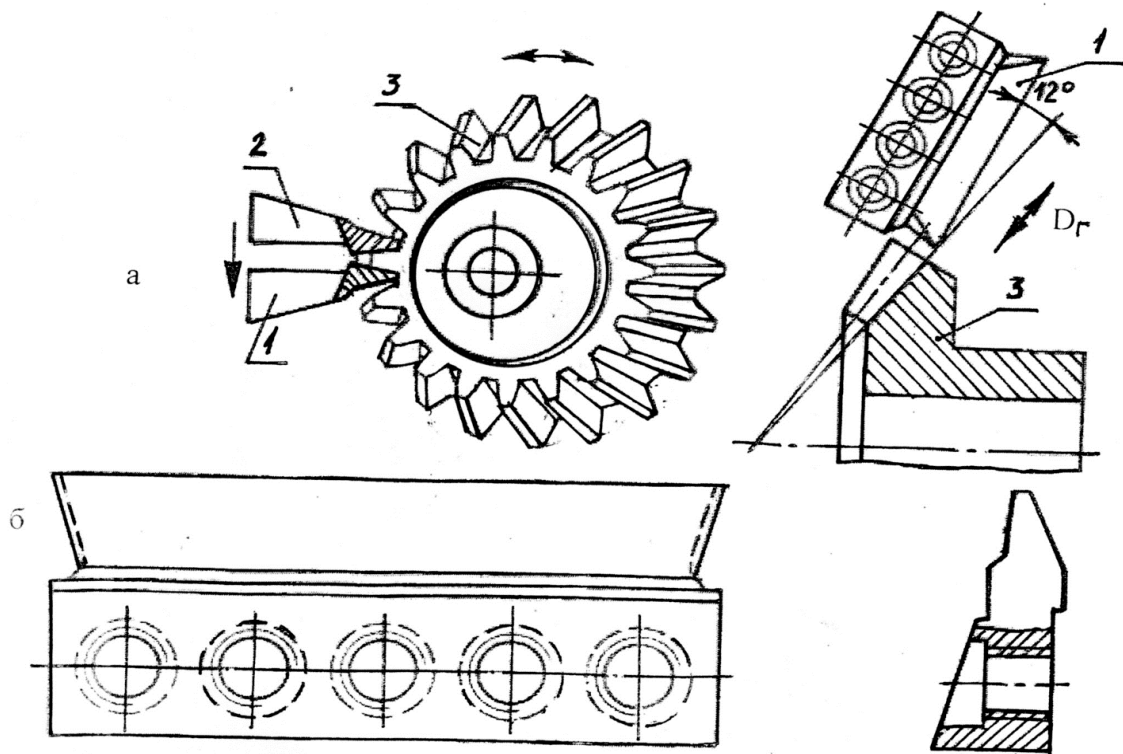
Резцы для нарезания прямозубого конического колеса:
